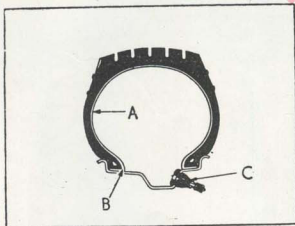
Corte transversal de neumático sin cámara, ilustrando la válvula instalada.
